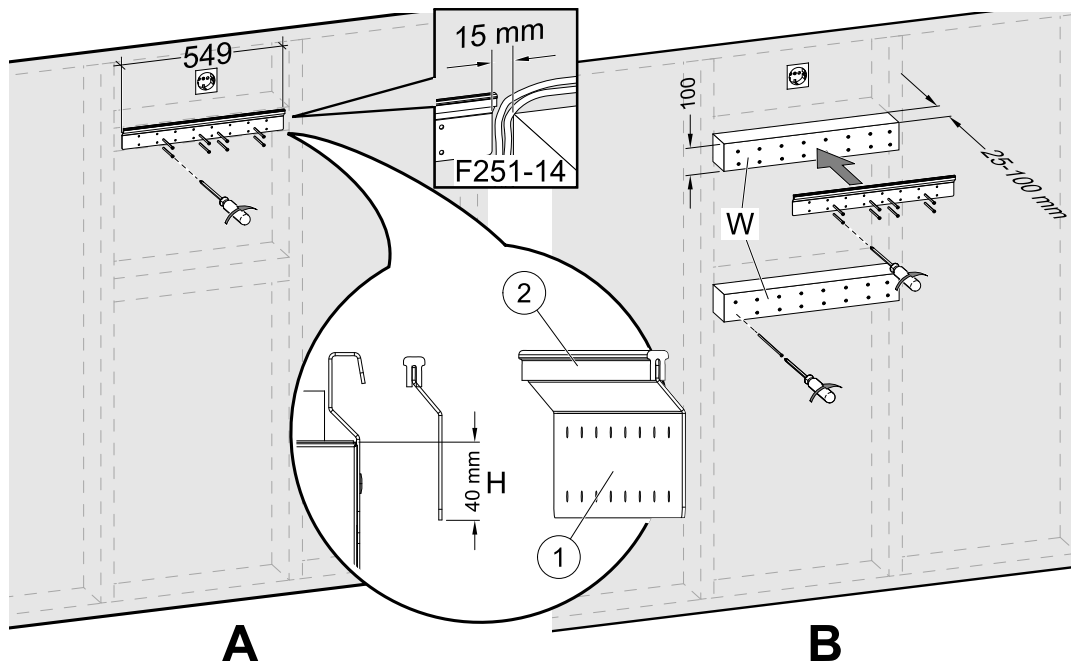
Installasjon av monteringsbrakett med eller uten utforing.
